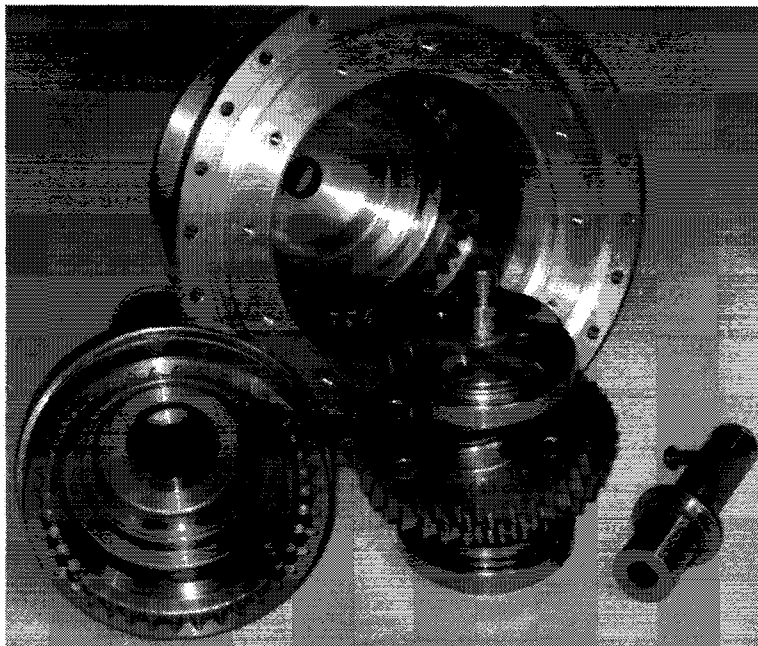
Элементы планетарного редуктора с цилиндроконическими зубчатыми зацеплениями
